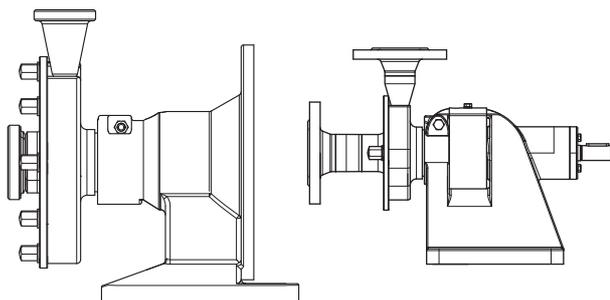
Machine incomplète : pompe sans moteur, accouplement et plaque de base, à l'exemple de la forme KF et L
